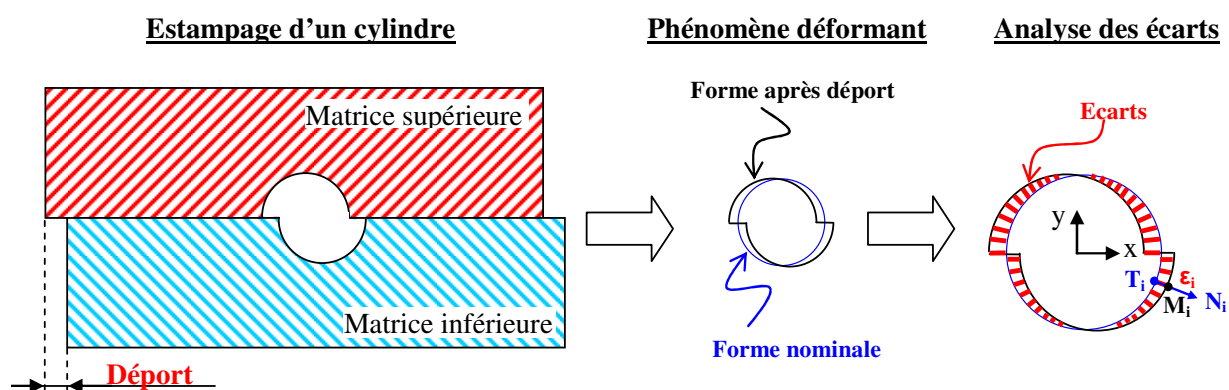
Défaut de forme causé par un déport des matrices en forge
